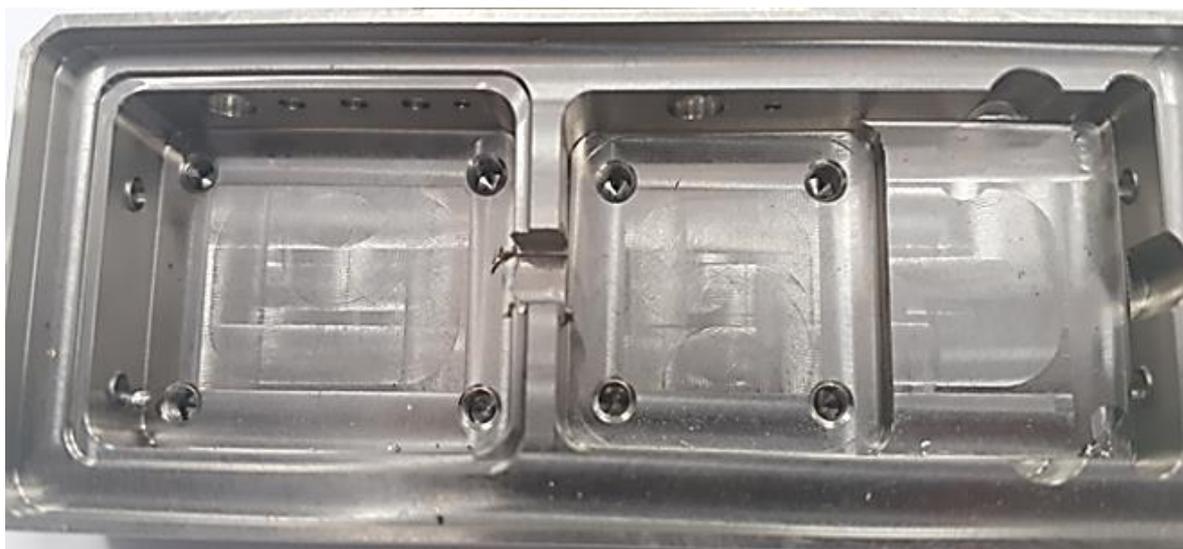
Дефекты в виде заусенцев на корпусе после обработки на фрезерном станке.
